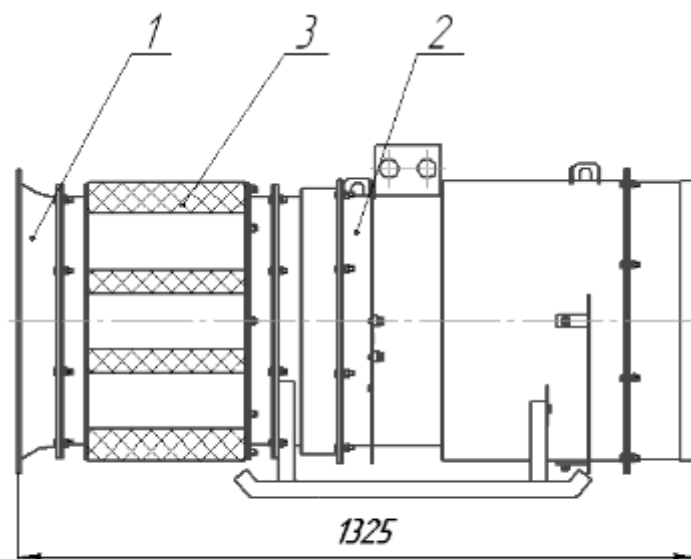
Вентилятор ВОЭ-5-01 с глушителем шума
